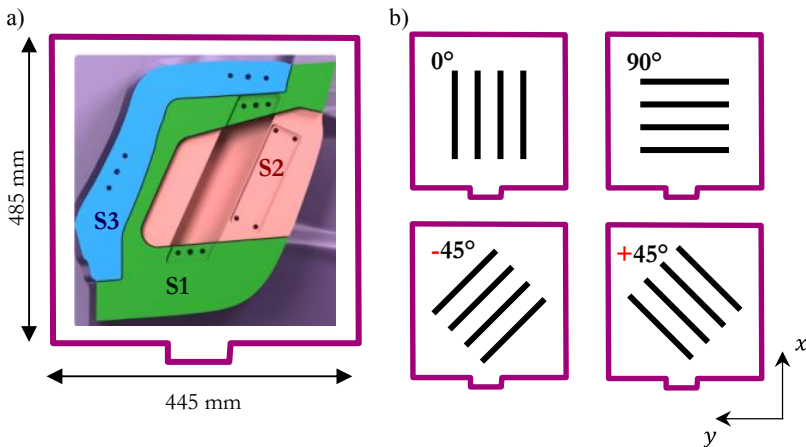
Zuschnitt der UD-Gelege für die Lampentopf-Umformversuche: a) Geometrie und Positionierung der Zuschnitte im Umformwerkzeug; b) Relativorientierung der einzelnen Halbzeuglagen.
